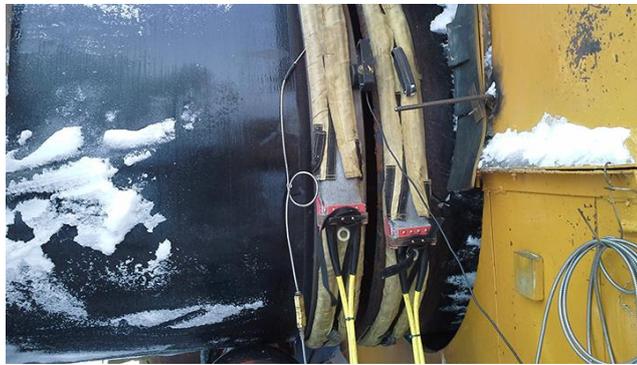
Junta de uma seção de duto a ser soldada pré-aquecida por indução [41]
